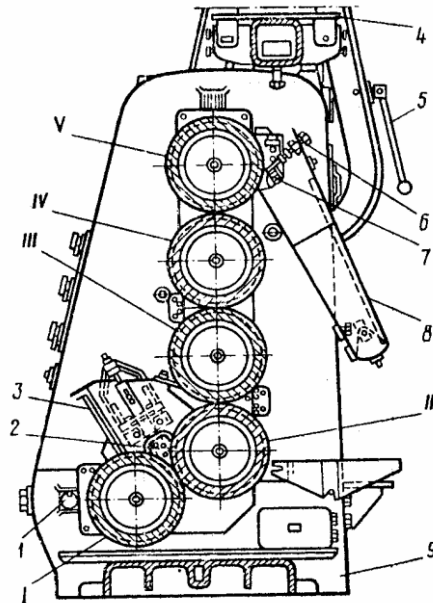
П'ятивалковий млин: I, II, III, IV, V – валки; 1 – запобіжний пристрій; 2 – скребок; 3 – воронка; 4 – плита; 5 – важіль; 6 – штурвал; 7 – ніж; 8 – похилий лоток; 9 – станина
